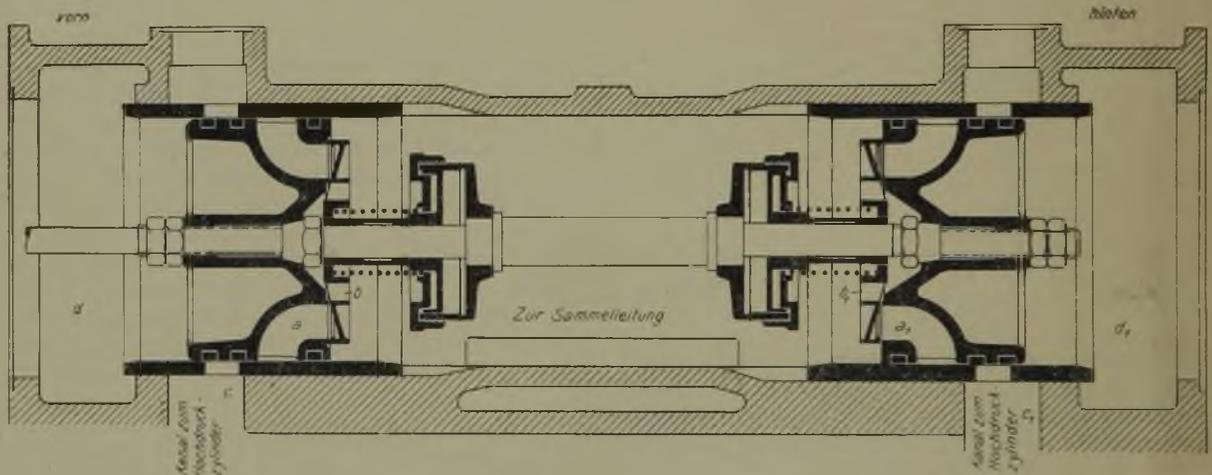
Kolbenschiebersteuerung des Kompressors.
